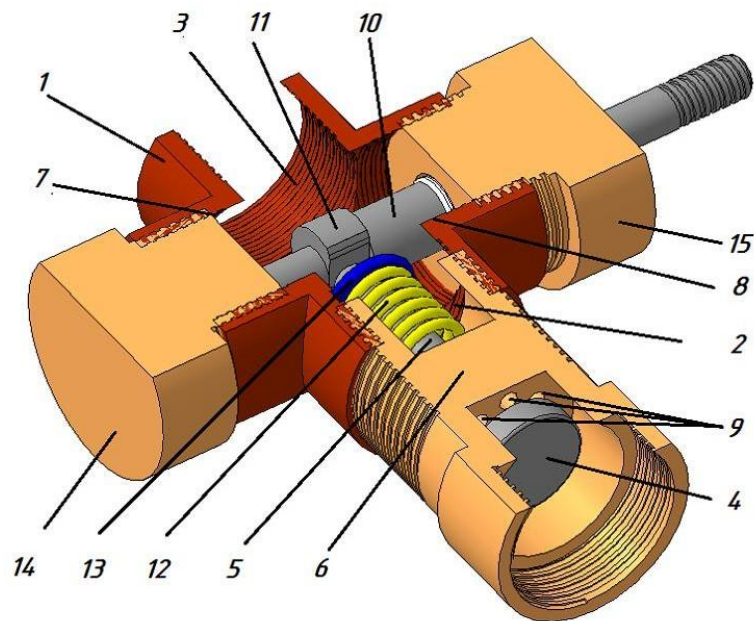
Конструкція ударного вузла: 1 – корпус; 2,3 – відповідно вхідний і вихідний отвори для протікання робочої рідини; 4 – ударний клапан; 5 – шток; 6 – втулка; 7, 8 – додаткові співвісний отвори; 9 – наскрізні клапани; 10 – вал; 11 – кулачок; 12 – пружина; 13 – стопорне кільце; 14 – центрувальна заглушка; 15 – напрямна втулка.
